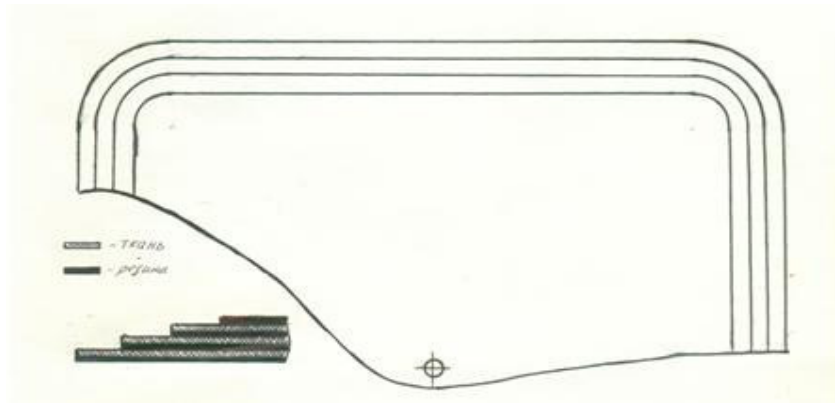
Заготовка из резиновой пластины для изготовления пневмобаллона
